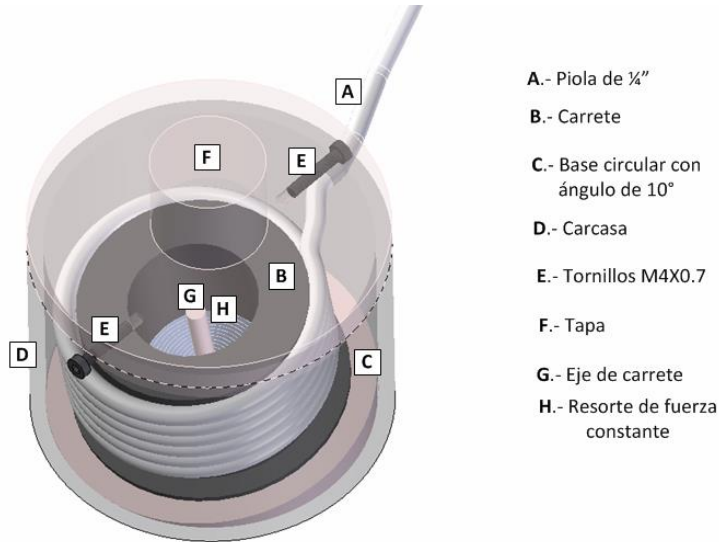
Subensamblado de mecanismo rebobinador con cordón embobinado.
